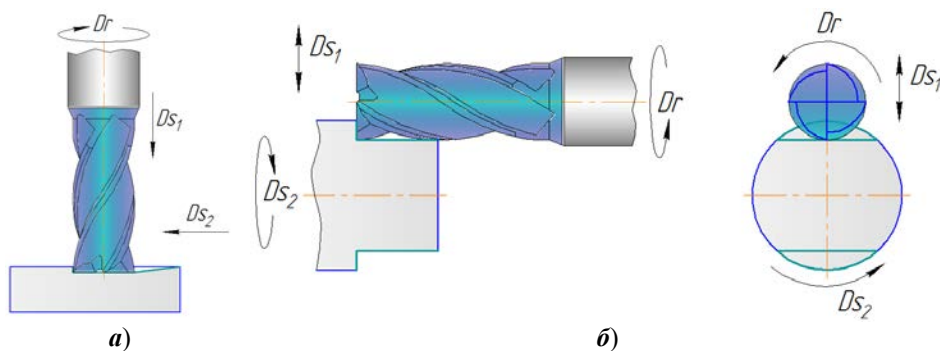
Схемы обработки с врезанием фрезы по касательной: *а* – плоской поверхности детали; *б* – плоской и цилиндрической поверхностей детали
